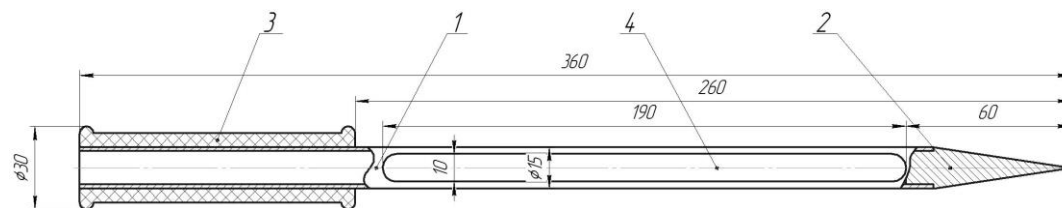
Щуп мешочный ПП ЩМ: 1 – пробоотборная трубка; 2 – конус; 3 –ручка; 4 – паз.
